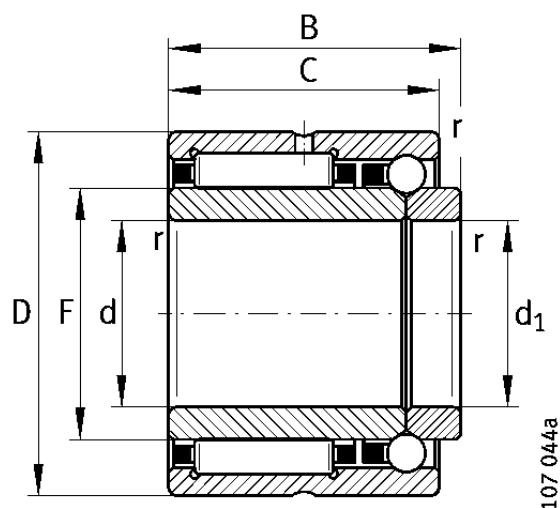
Габаритные размеры серии NKIB ф INA
